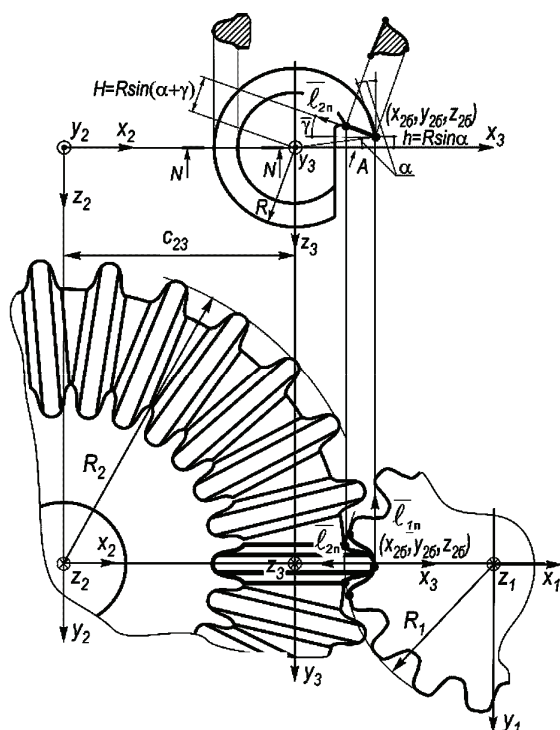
К расчету профиля сборного долбяка с призматическими фасонными резами
